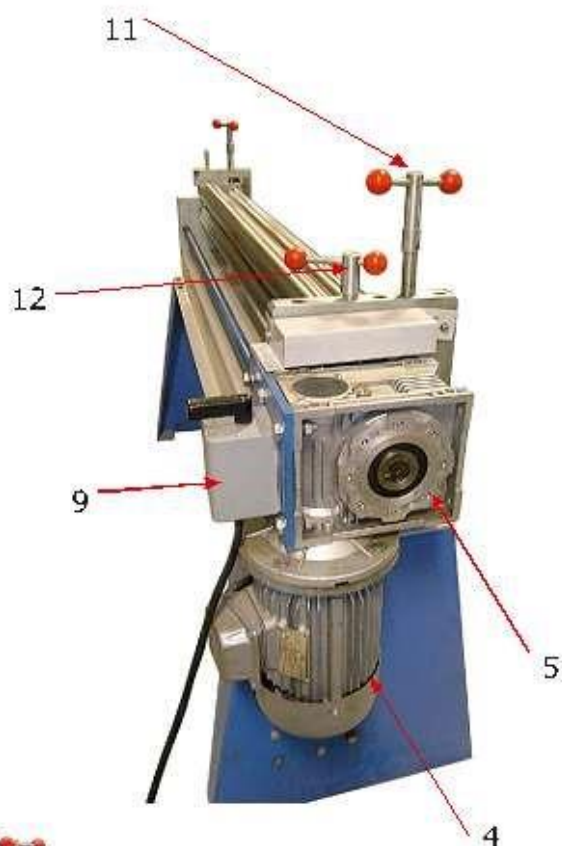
Ручка регулирующая заднего вала (вид слева)
